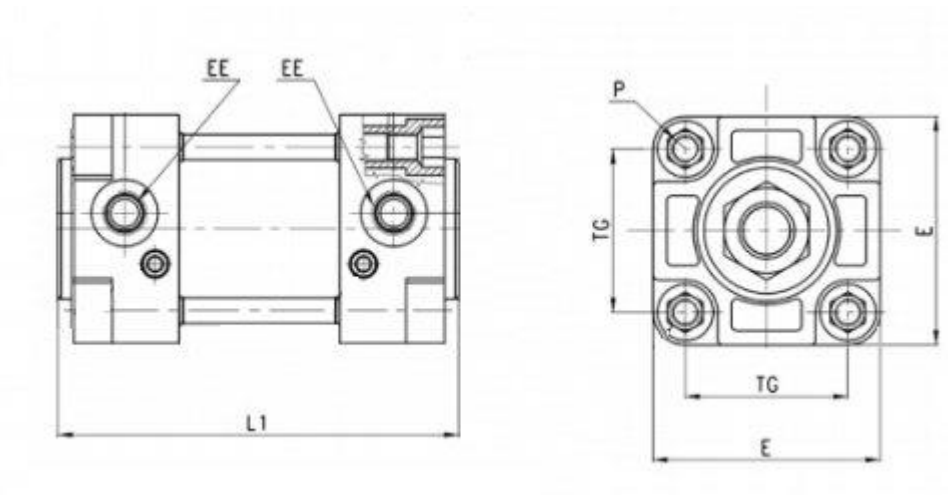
Габаритные размеры ресиверов 40N3L100A0600M
